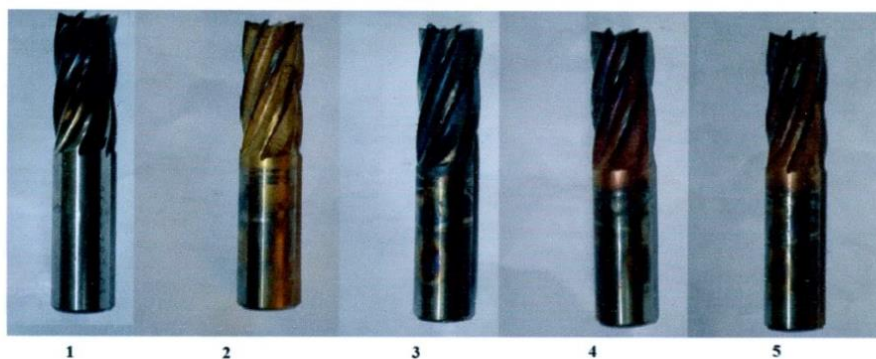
Фреза без покрытия(1) и фрезы с покрытиями (2-5)
